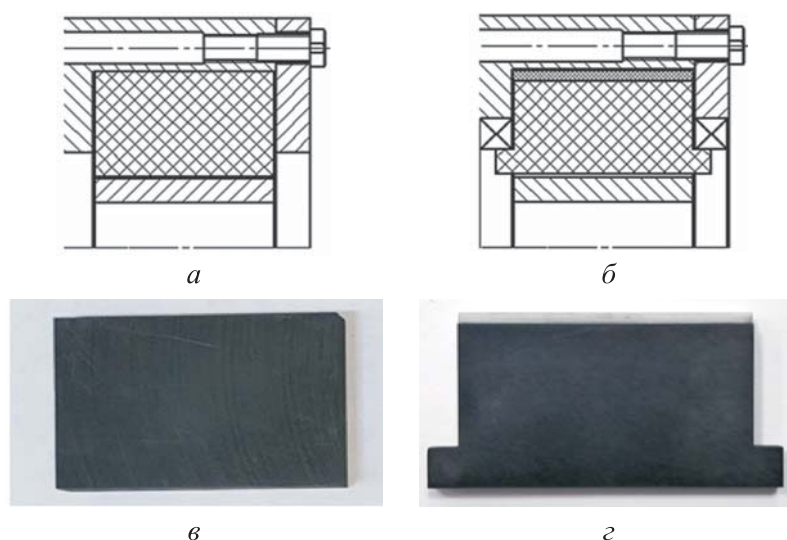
Уплотнительные пластины несмазываемой ступени роторно-пластинчатого компрессора с традиционной (а, в) и новой (б, г) трибологическими схемами
